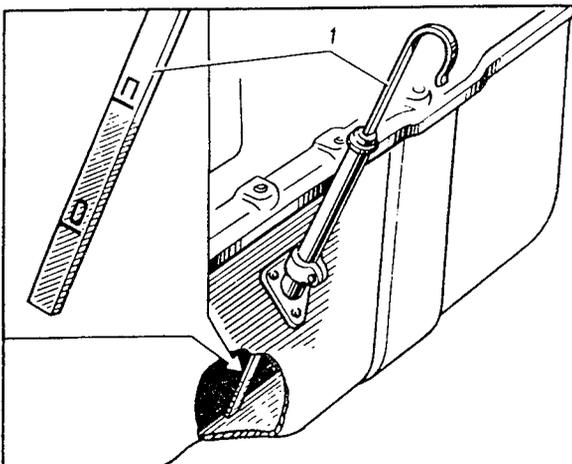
Prüfung des Ölstandes im Motorkurbelgehäuse:
